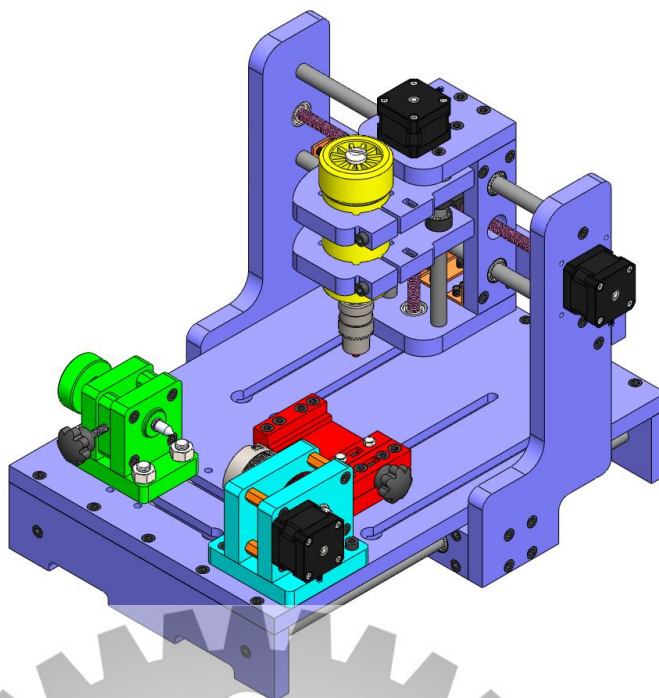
Тривимірний модель токарно-фрезерного верстата
